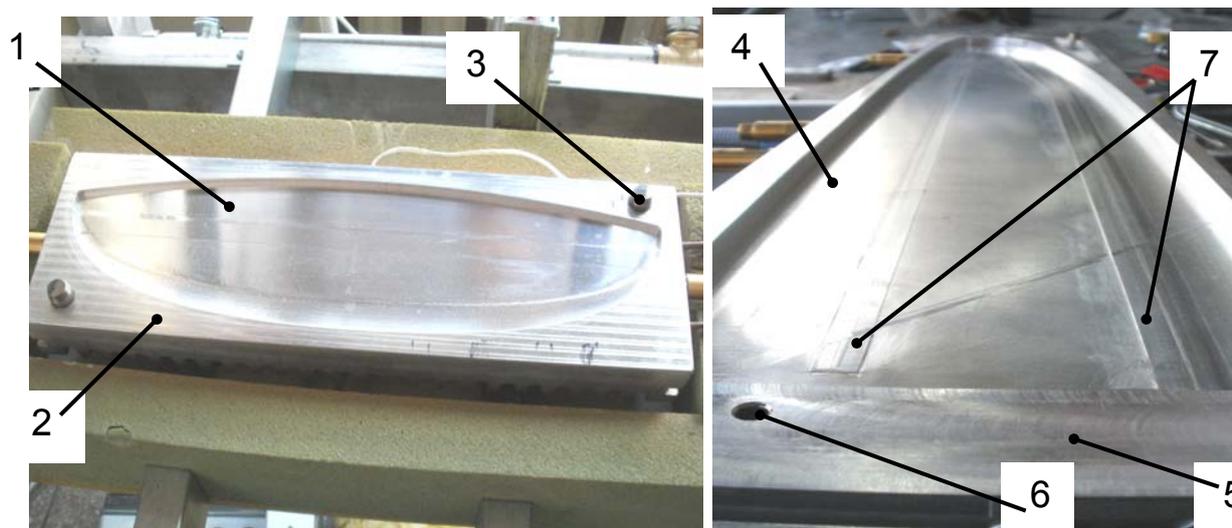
Элементы матрицы постформинга: 1 – формаобразующая поверхность пуансона; 2 – корпус пуансона; 3 – направляющая-фиксатор пуансона; 4 – формаобразующая поверхность матрицы; 5 – корпус матрицы; 6 – фиксирующее отверстие матрицы; 7 – формаобразующие ребра продольного силового набора
